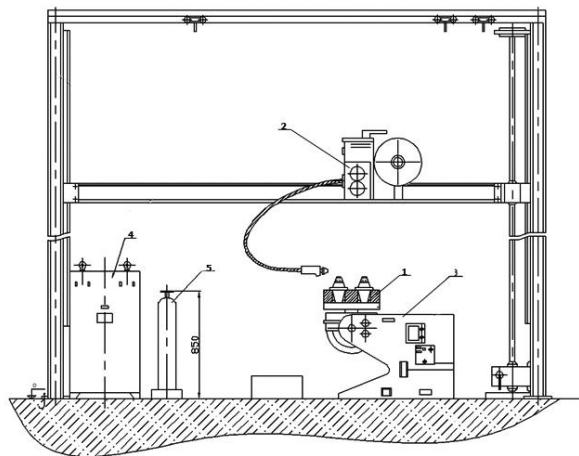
Устаткування напівавтоматичного наплавлення із застосуванням самозахисного порошкового дроту:
